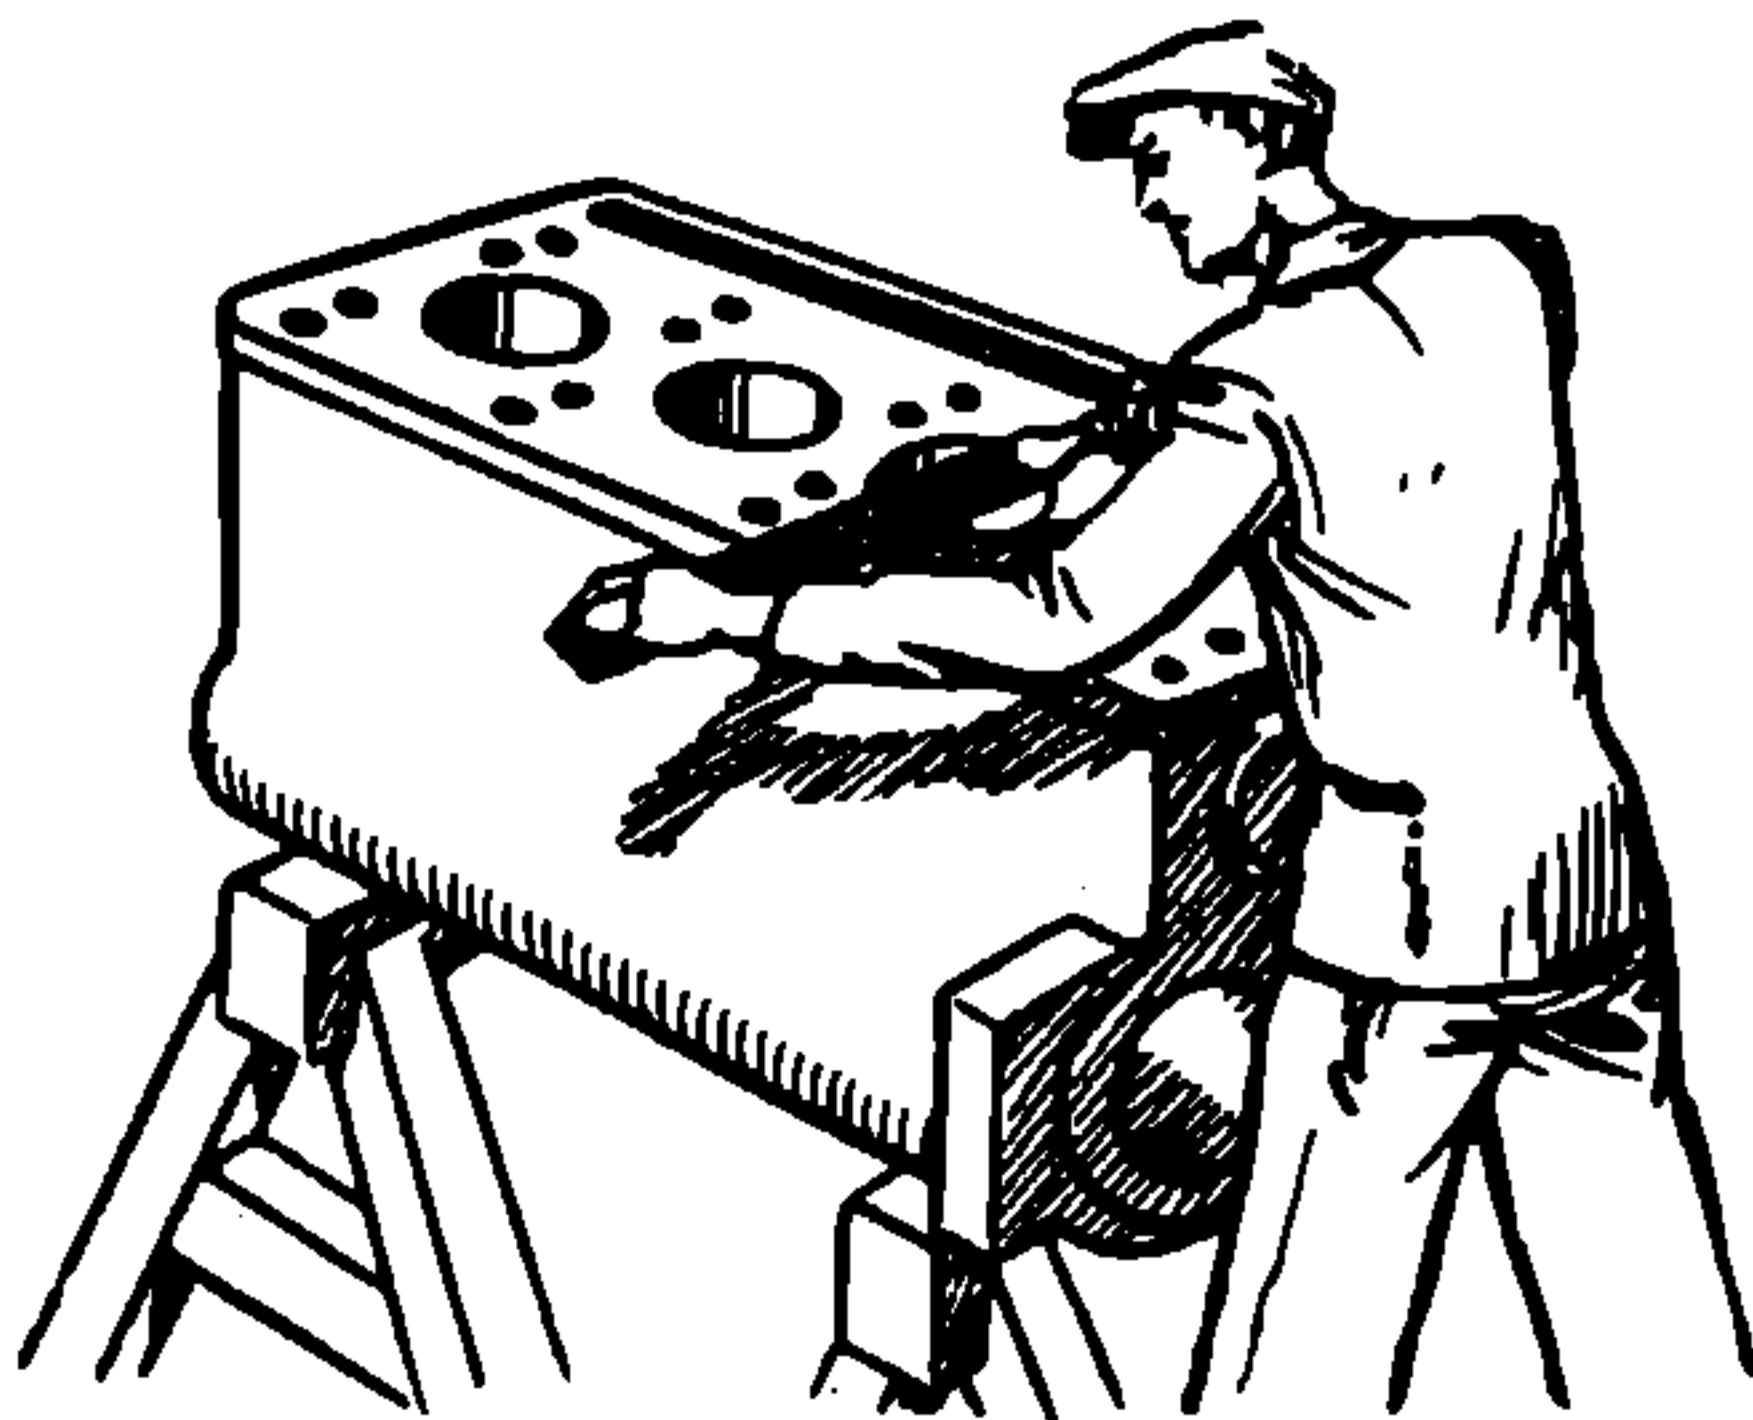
Entgraten eines maschinell bearbeiteten Werkstückes
